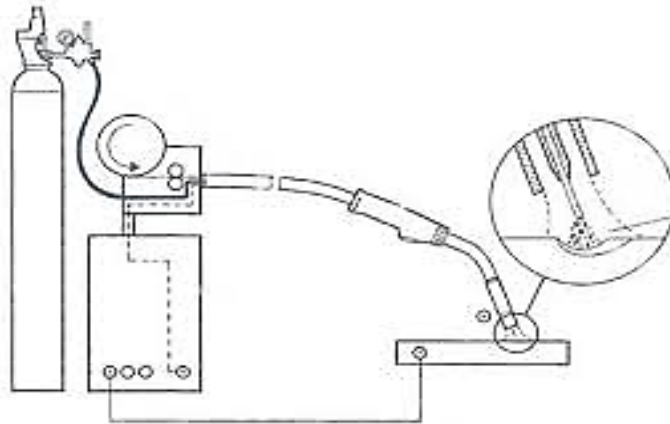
Soldadura con electrodo consumible (método MIG y MAG).
